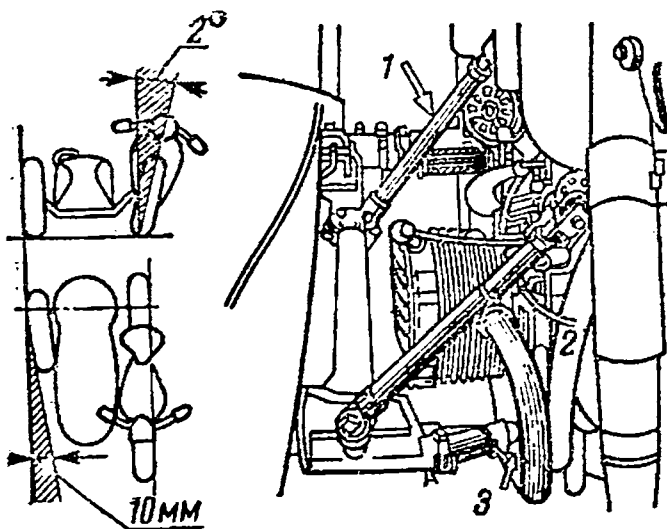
Регулировка развала и схождения колес мотоцикла и бокового прицепа:
